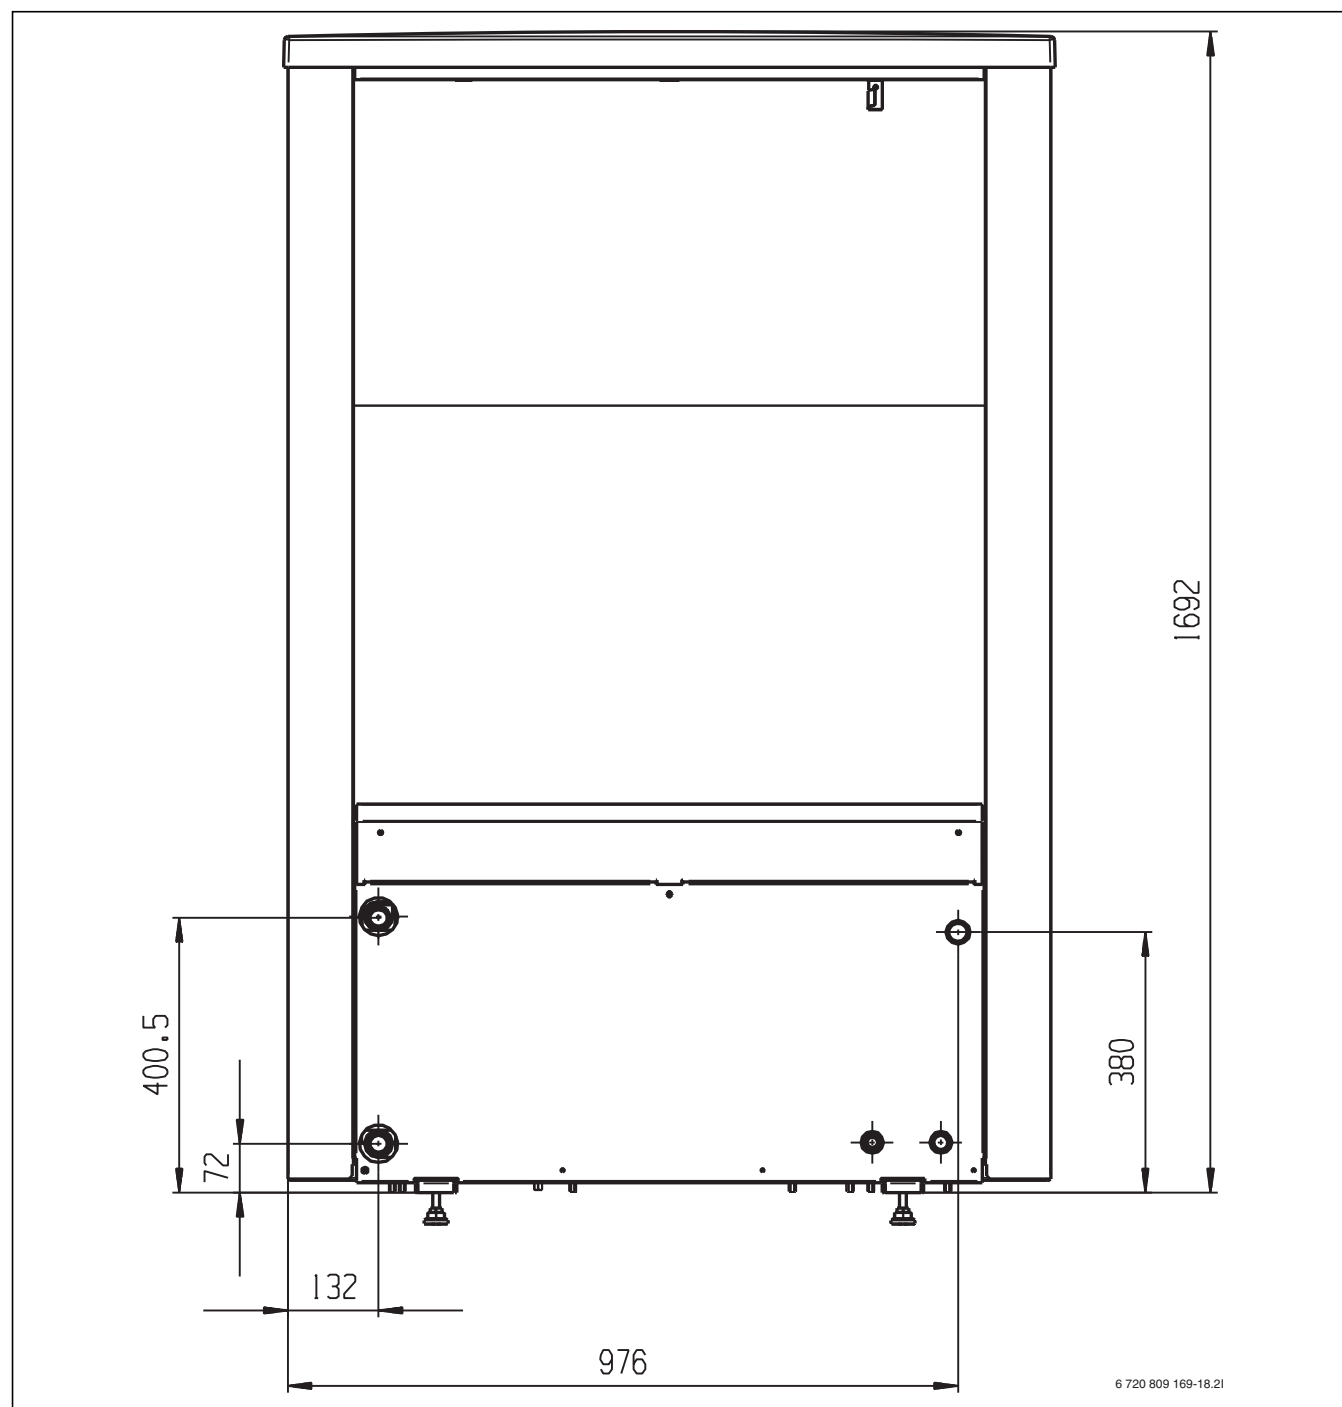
Rozměry a připojení tepelného čerpadla, zadní část Air X 50-90
